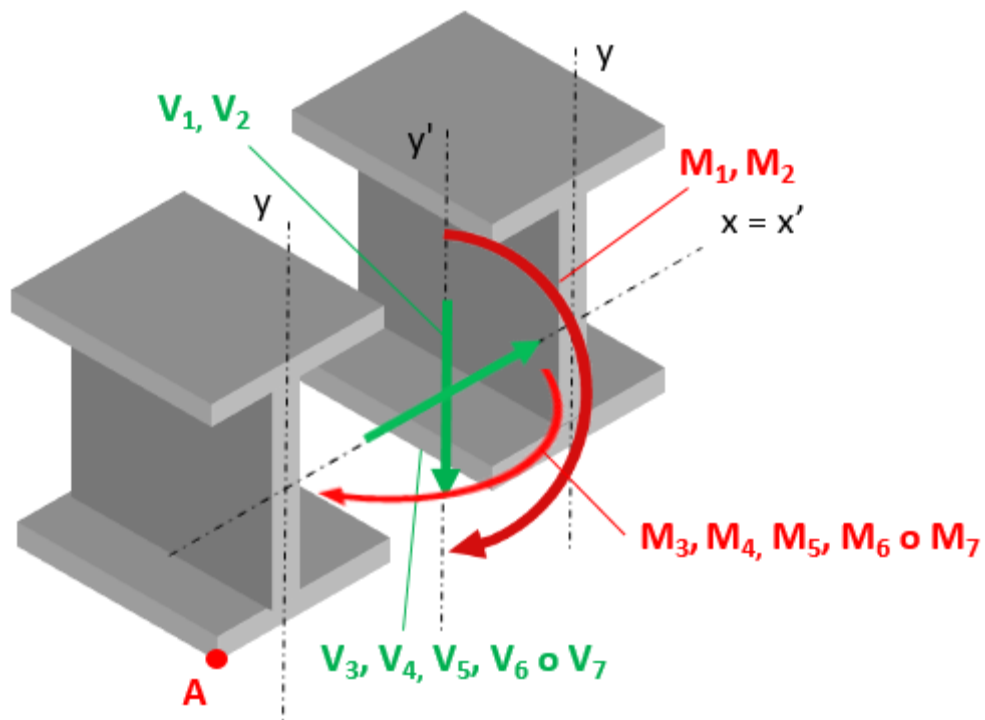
Esfuerzos en la sección más crítica de la pluma para el caso de grúa con contrapeso.
